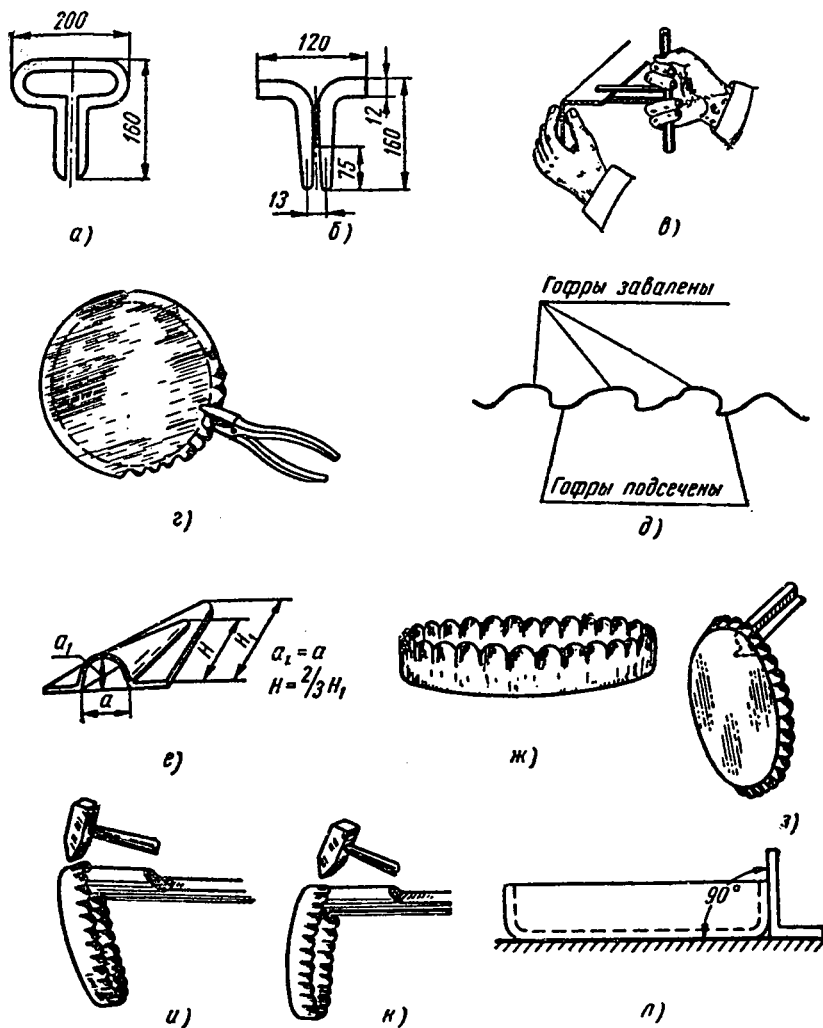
Посадка металла при изготовлении днаща ручным способом:
